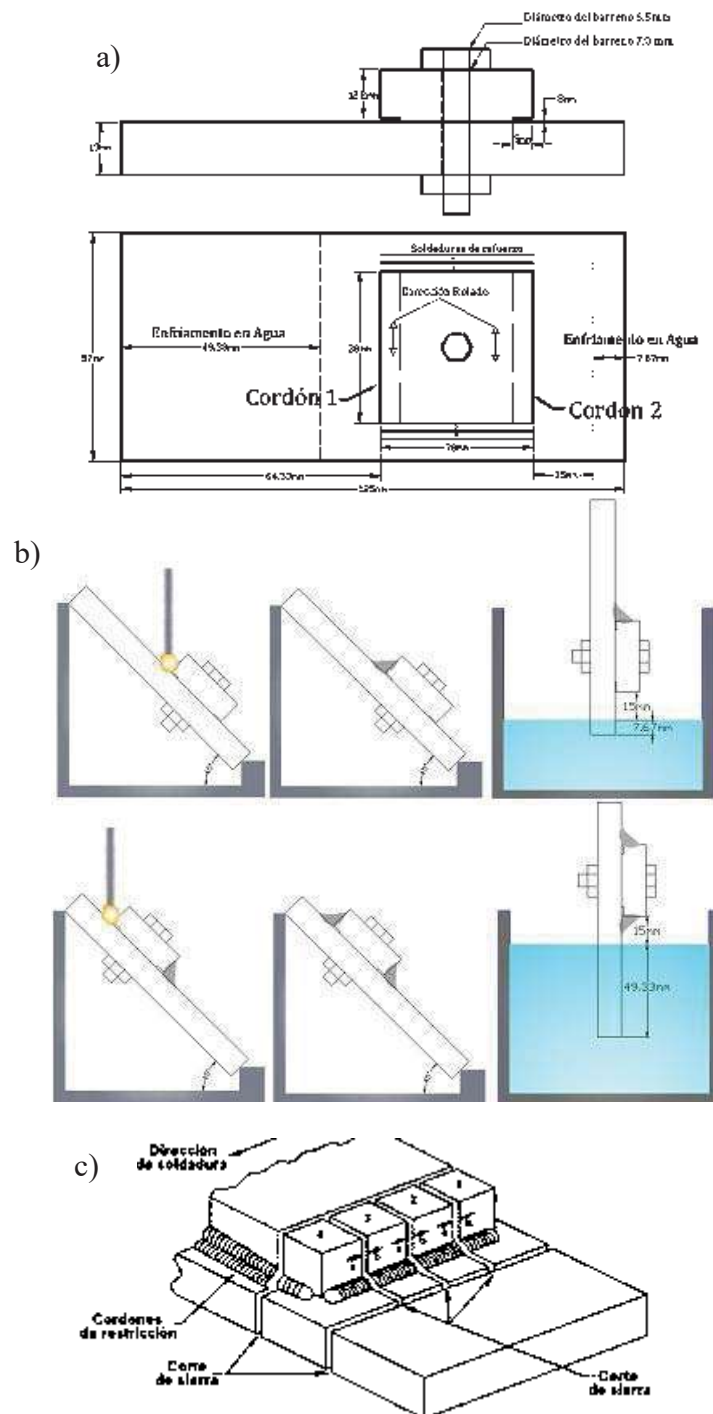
Dimensiones del ensayo CTS (a) montaje (b), y cortes para inspección (c).
